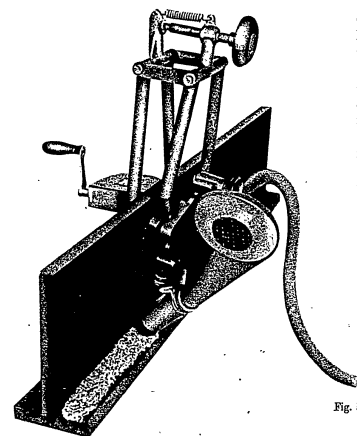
Специализированный держатель ДШ-27 для приварки ребер жесткости к балкам
